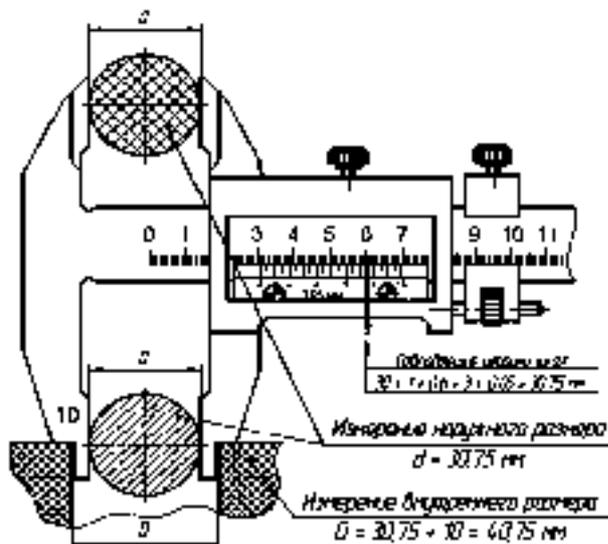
Измерение размеров деталей штангенциркулем типа II
